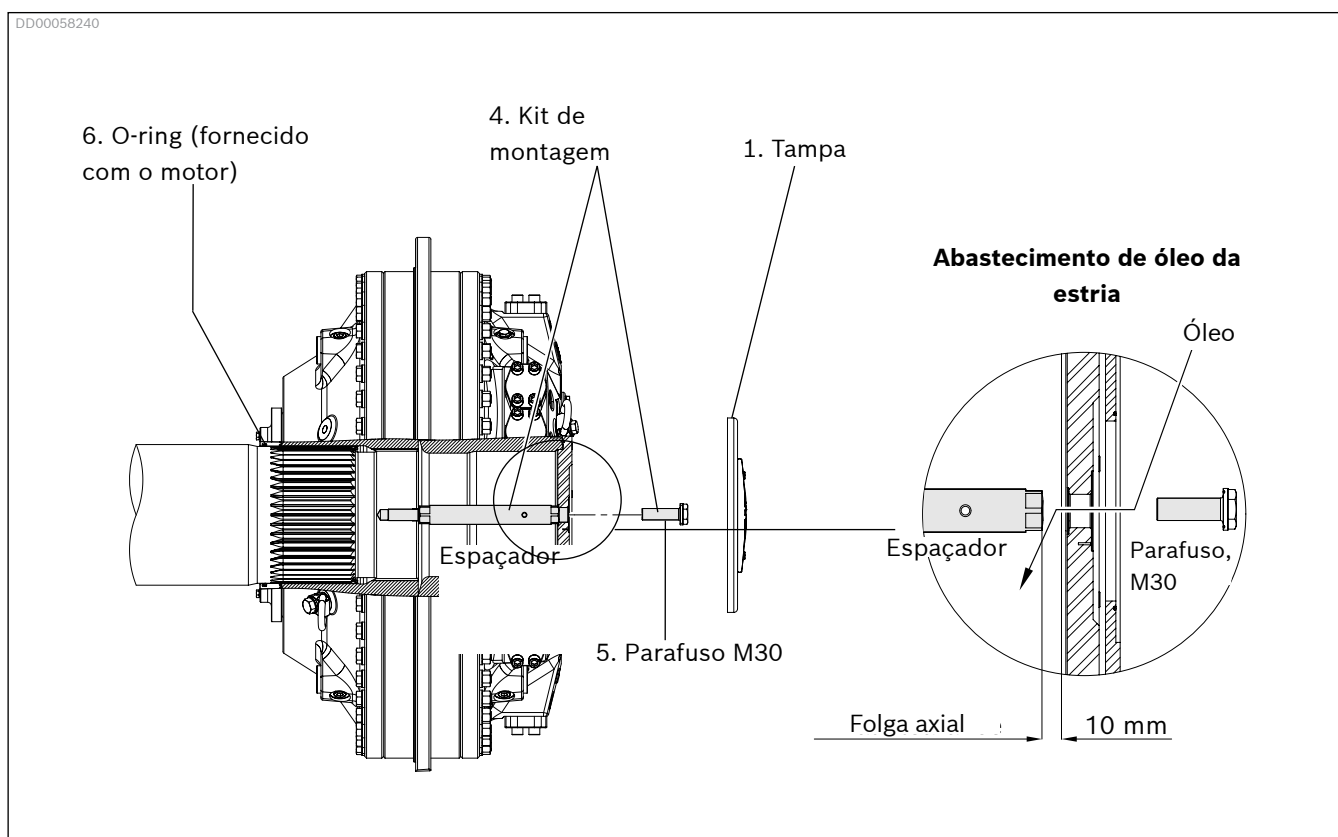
Fixação do motor com estria com o kit de montagem, montagem horizontal
